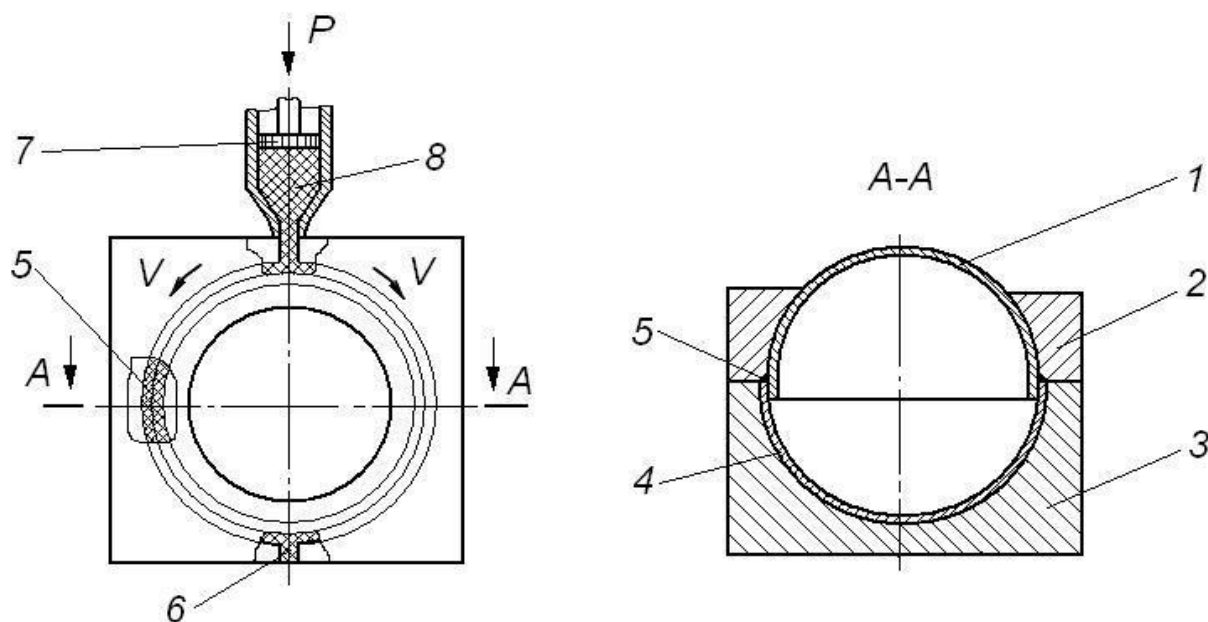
Схема зварювання шляхом лиття під тиском сферичної конструкції: 1 – верхня півсфера; 2, 3 – частини прессформи; 4 – нижня півсфера; 5 – зварний шов; 6 – контрольний отвір; 7 – машина литва; 8 – присадочний матеріал; V – напрямок руху розплавленого матеріалу.
